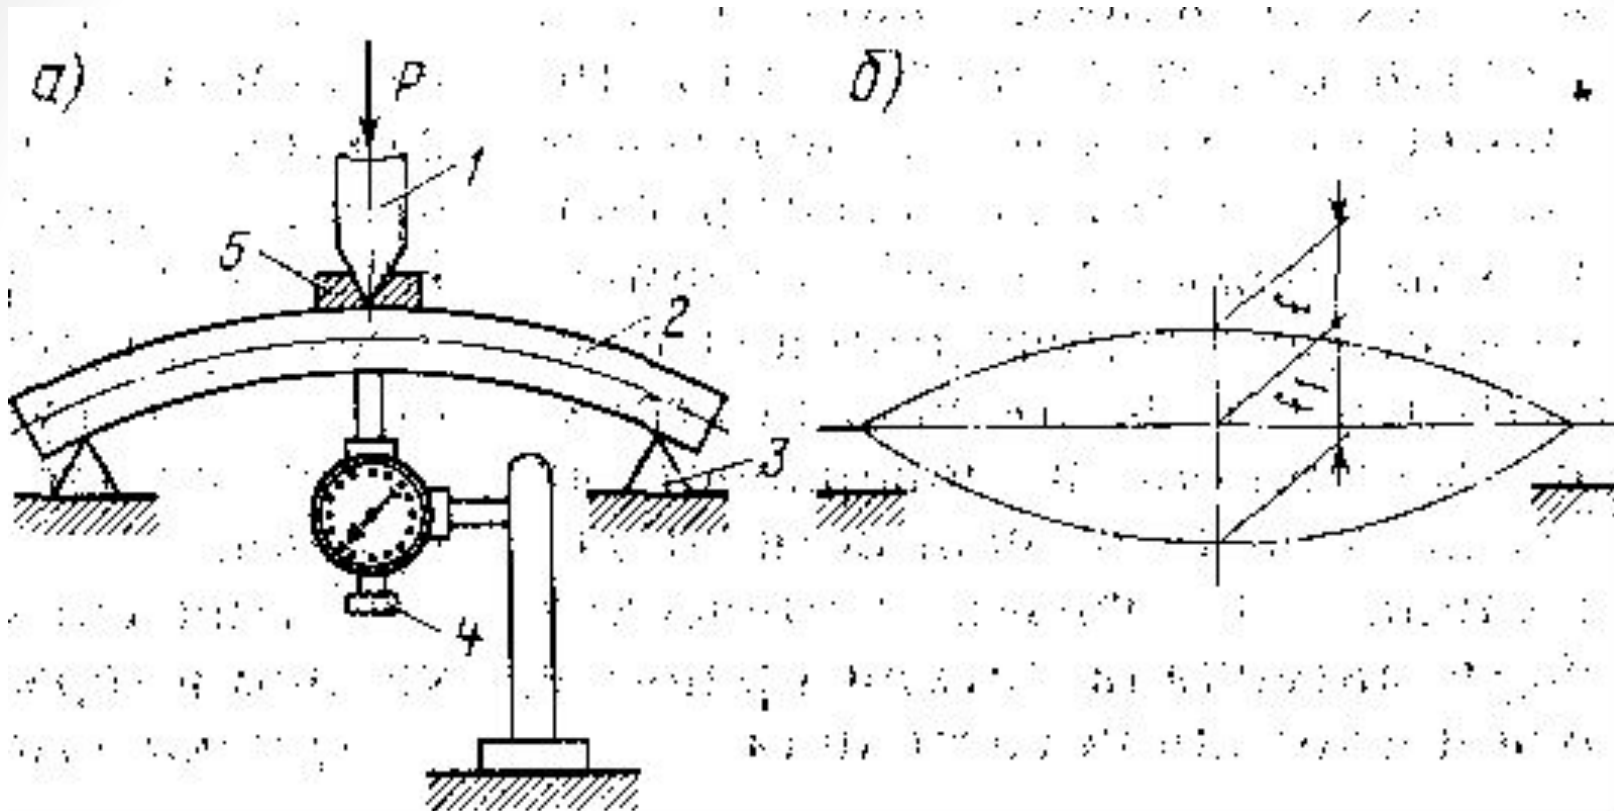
Схема холодной правки вала: а — монтажная; б — расчетная
